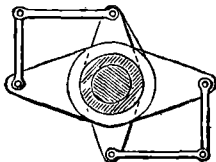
Leviers d'entraînement du dernier truck Short.
